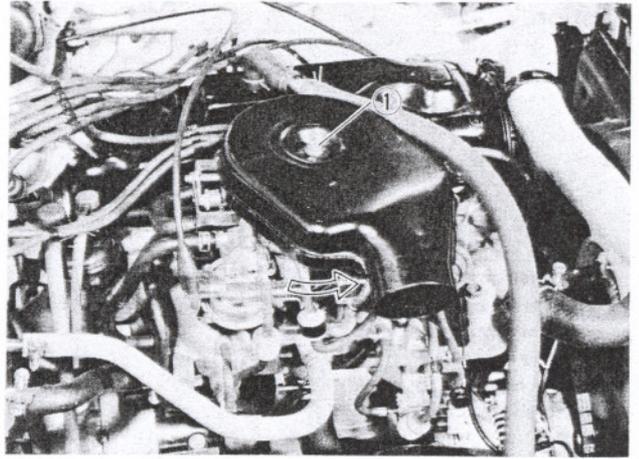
1. Ecrou du boîtier de prise d'air
